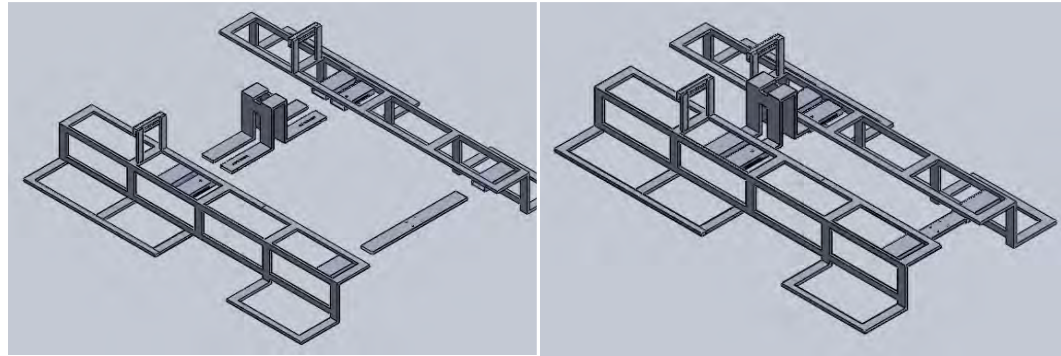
Vista explosionada del conjunto de elementos descritos anteriormente que van ensamblados al chasis.
